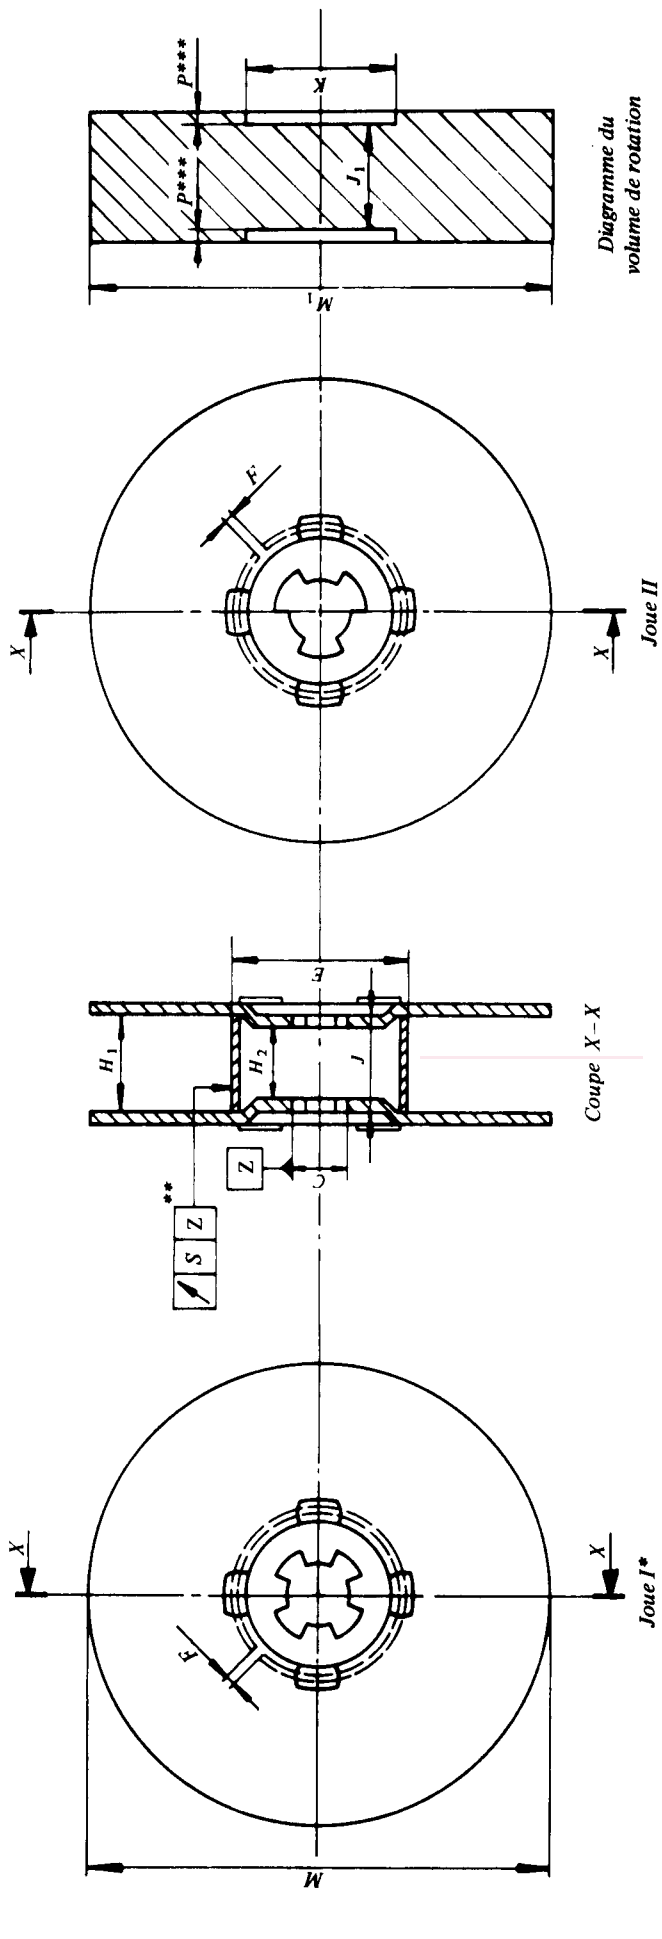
Dimensions des bobines de chargement en plein jour pour film cinématographique double 8 mm
